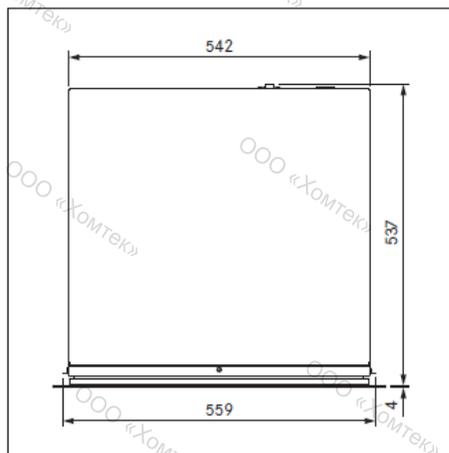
Размеры прибора, модель MSS140, вид сверху
